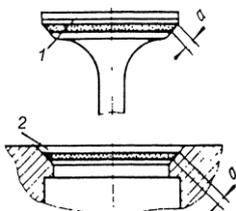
Прибор для проверки качества притирки клапанов
